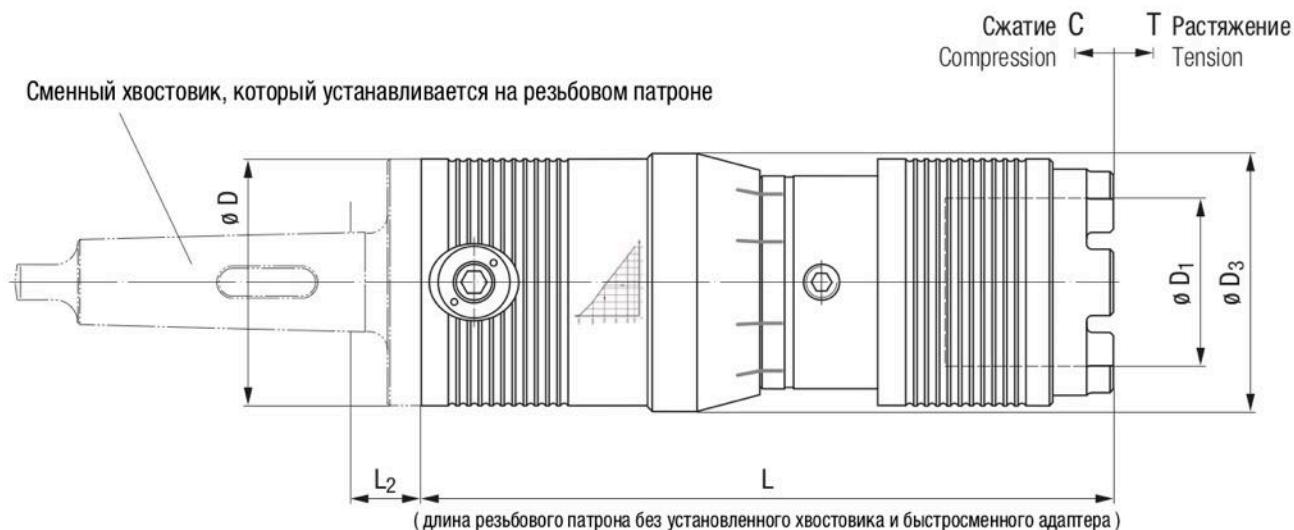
Основные размеры резьбовых патронов серии HF с быстросменными адаптерами
